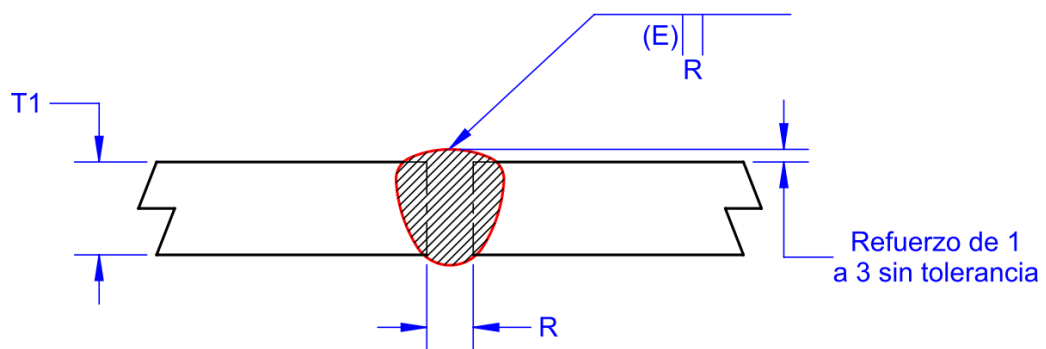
1 Soldadura a tope de canal cuadrada
